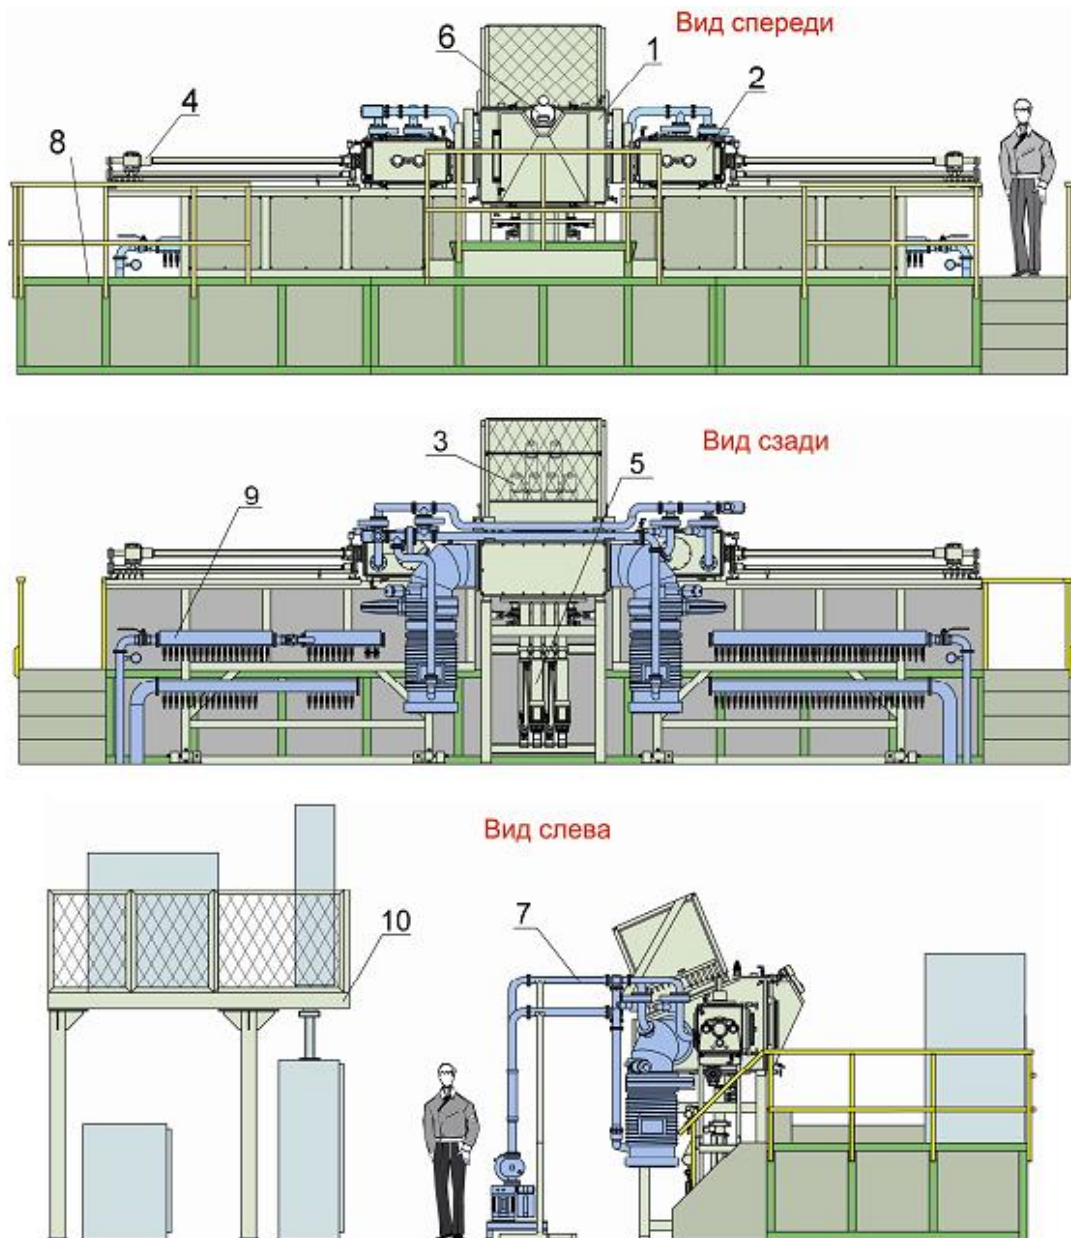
Загальна схема установки L-8: а – вид спереду; б – вид ззаду; в – вид зліва (1 - камера технологічна; 2 - камера шлюзова; 3 - електронні гармати; 4 - механізм подачі касети (виробів); 5 - механізм подачі зливка; 6 - оглядова система; 7 - вакуумна система; 8 - майданчик обслуговування; 9 - система охолодження; 10 - платформа високовольного джерела живлення)
